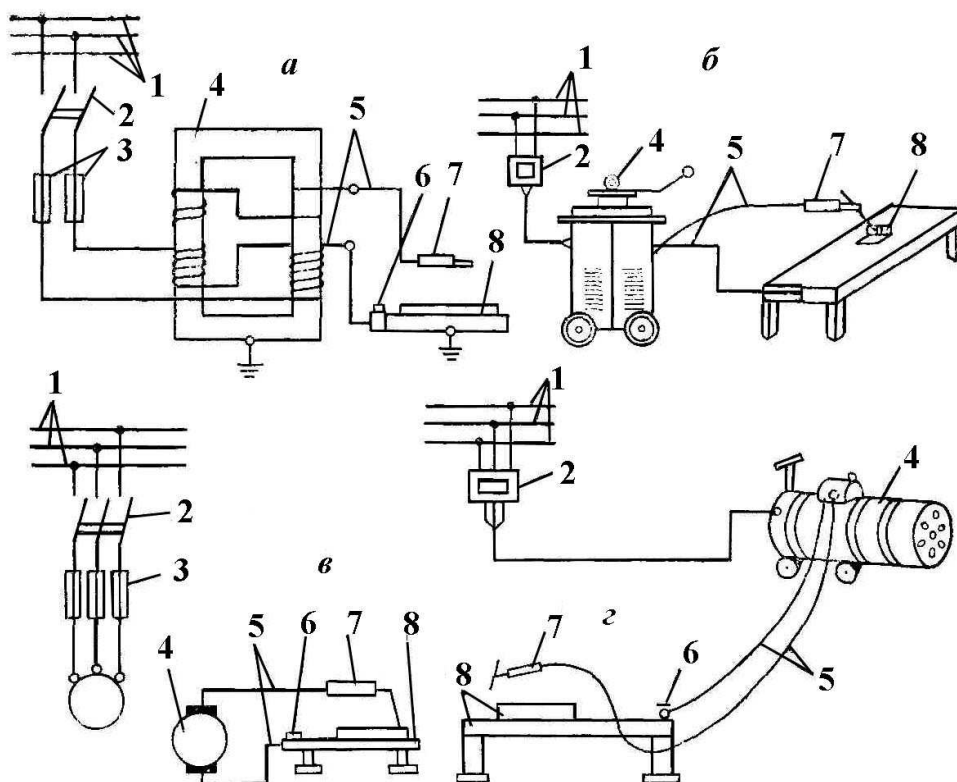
Пристрій для ручного електродугового зварювання:
